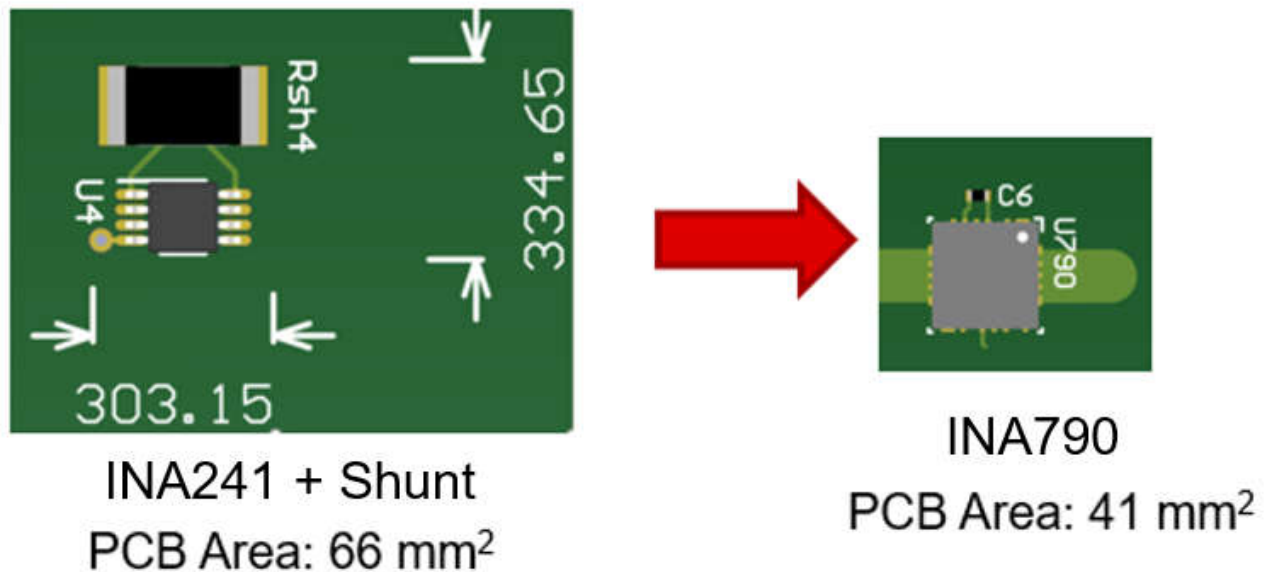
INA790 使用标准 MSOP + 分流器可减少 38% 的 PCB 空间
